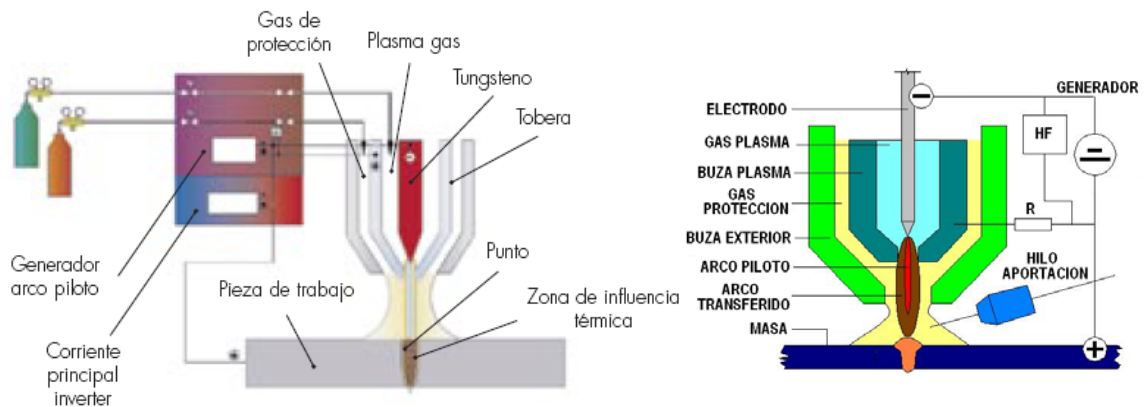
Elementos que intervienen en el proceso de soldadura por arco plasma (PAW)
